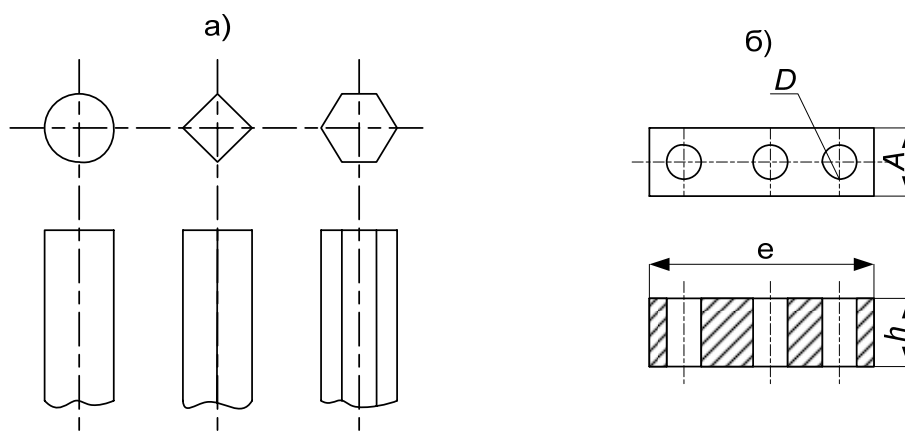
Схемы инструмента и обрабатываемой заготовки:
